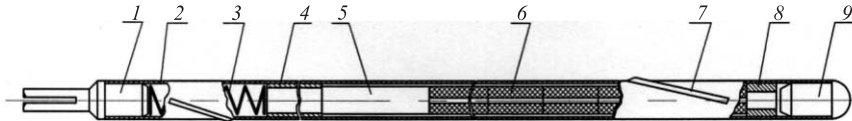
Тепловыделяющий элемент реактора ИБР-2: 1 — наконечник верхний; 2 — оболочка; 3 — пружина; 4 — вставка; 5 — отражатель; 6 — таблетки активной части; 7 — проволока; 8 — втулка; 9 — заглушка
